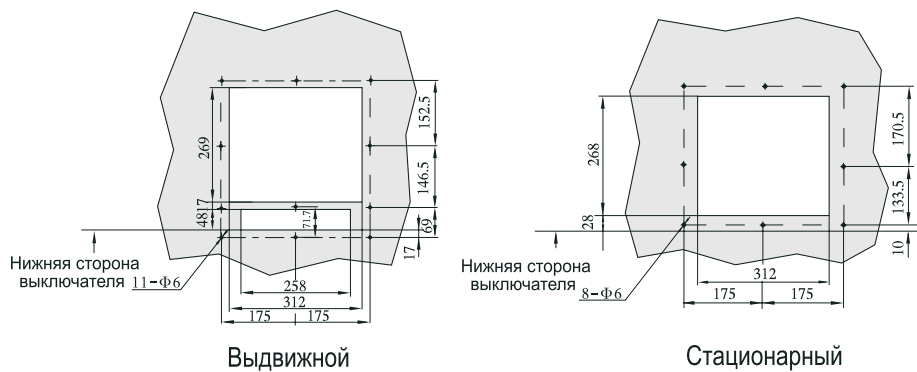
Габаритные размеры рамки обрамления выреза в двери для выключателей типоразмера D
